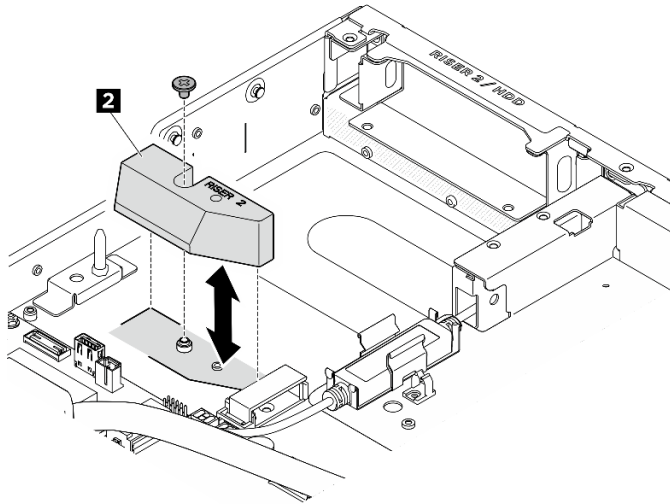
Entfernen der DPU-Luftführung aus dem Gehäuse
